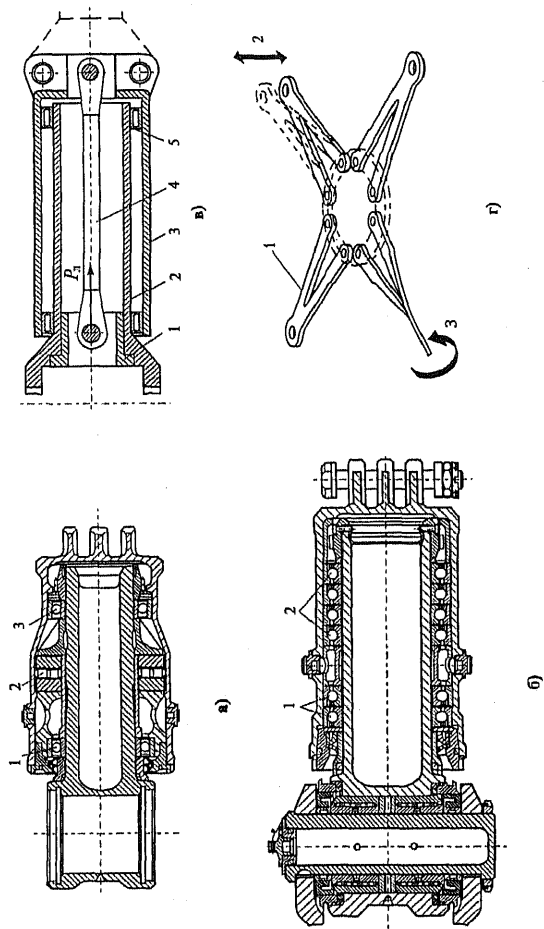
Конструктивно-силовая схема осевых шарниров втулки несущего винта:
